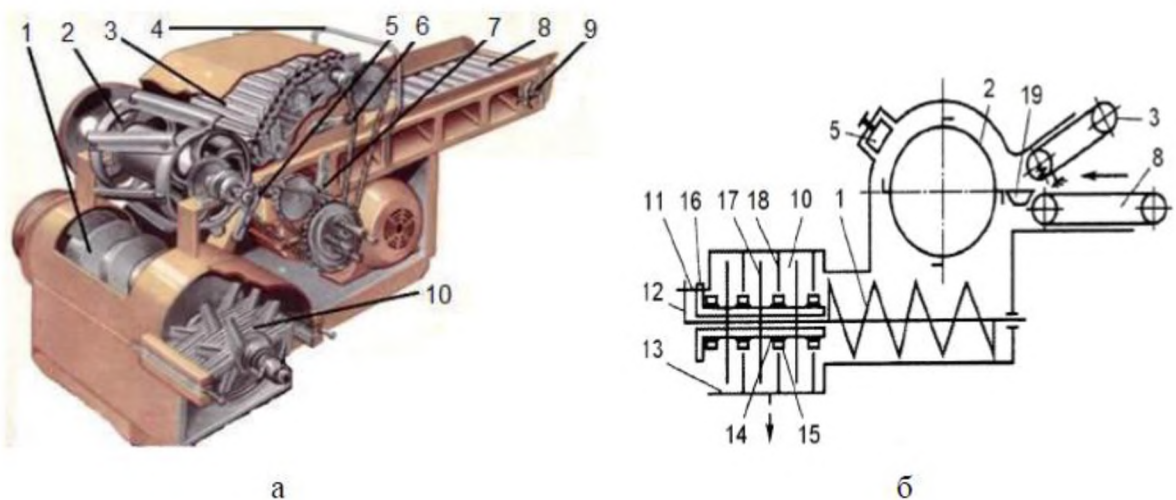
Загальна будова (а) та конструктивна-функціональна схема (б) подрібнювача ИКВ-5А «Волгарь-5»: 1 – шнек; 2 – ножовий барабан; 3 – похилий конвеєр; 4 – механізм керування конвеєрами; 5 – натяжний пристрій ланцюгового передавача редуктора; 6 – натяжний пристрій ланцюгового передавача похилого конвеєра; 7 – натяжний пристрій ланцюгового передавача горизонтального конвеєра; 8 – горизонтальний конвеєр; 9 – натяжний пристрій горизонтального конвеєра; 10 – подрібнювальний апарат другого ступеня; 11 – зрізний штифт; 12 – фланець вала шнека; 13 – опора нерухомих ножів; 14 –
